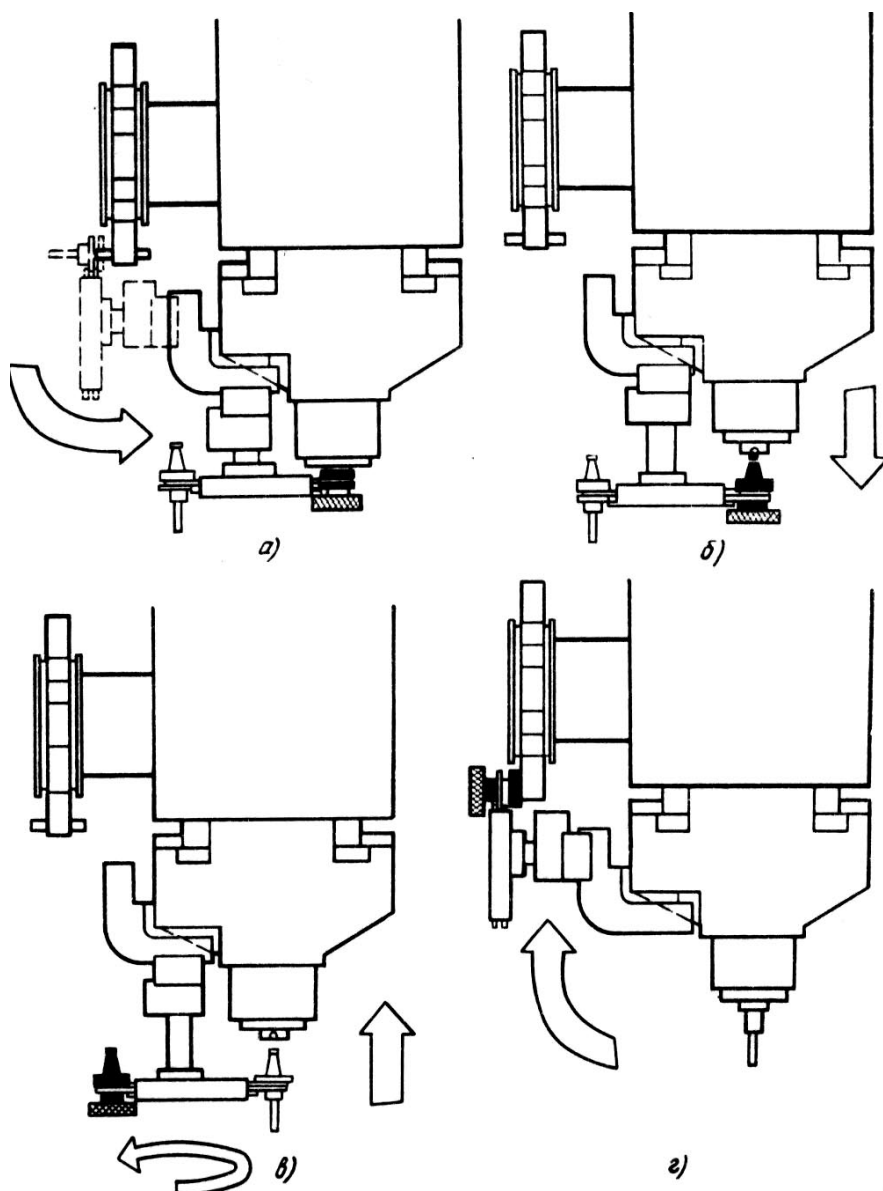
Схема передачи инструмента из инструментального магазина в шпиндель станка: *а* – неполное положение; *б* – вывод инструмента из шпинделя; *в* – установка в шпиндель нового инструмента; *г* – установка инструмента в магазин
